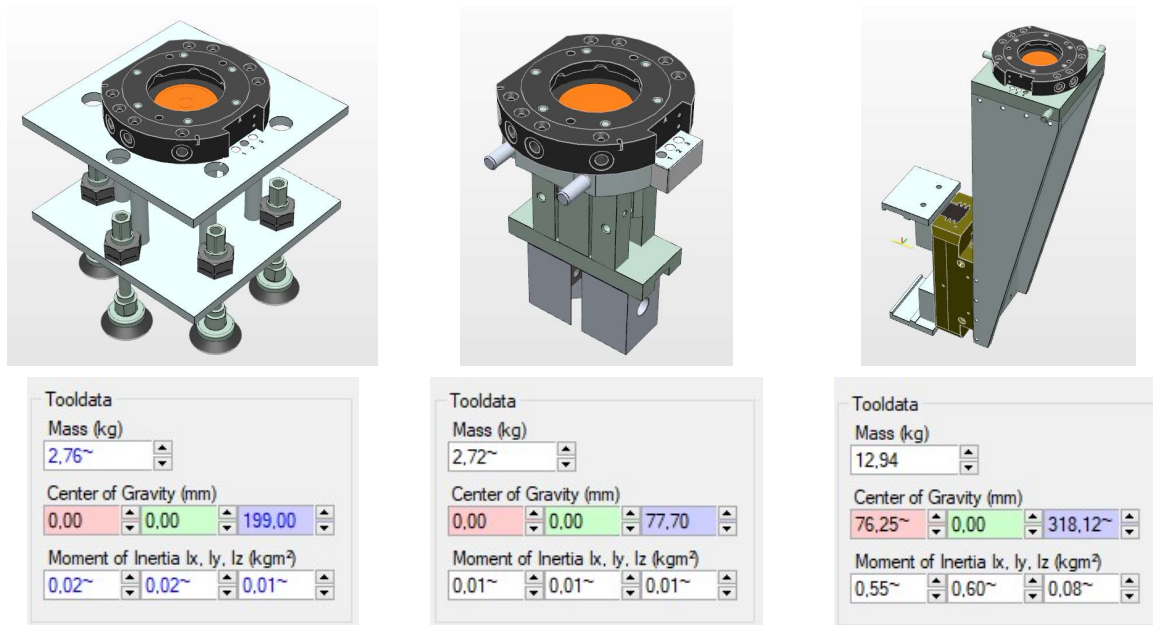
Gripper s chapadlem SMC (vlevo) a Gripper s chapadlem Schunk (vpravo)
